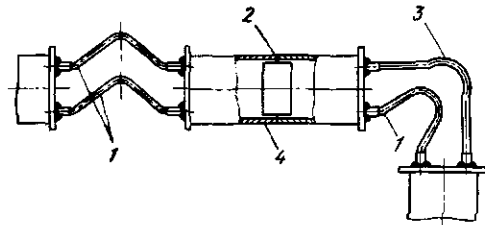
Установка компенсаторов и стыковочных колец:
